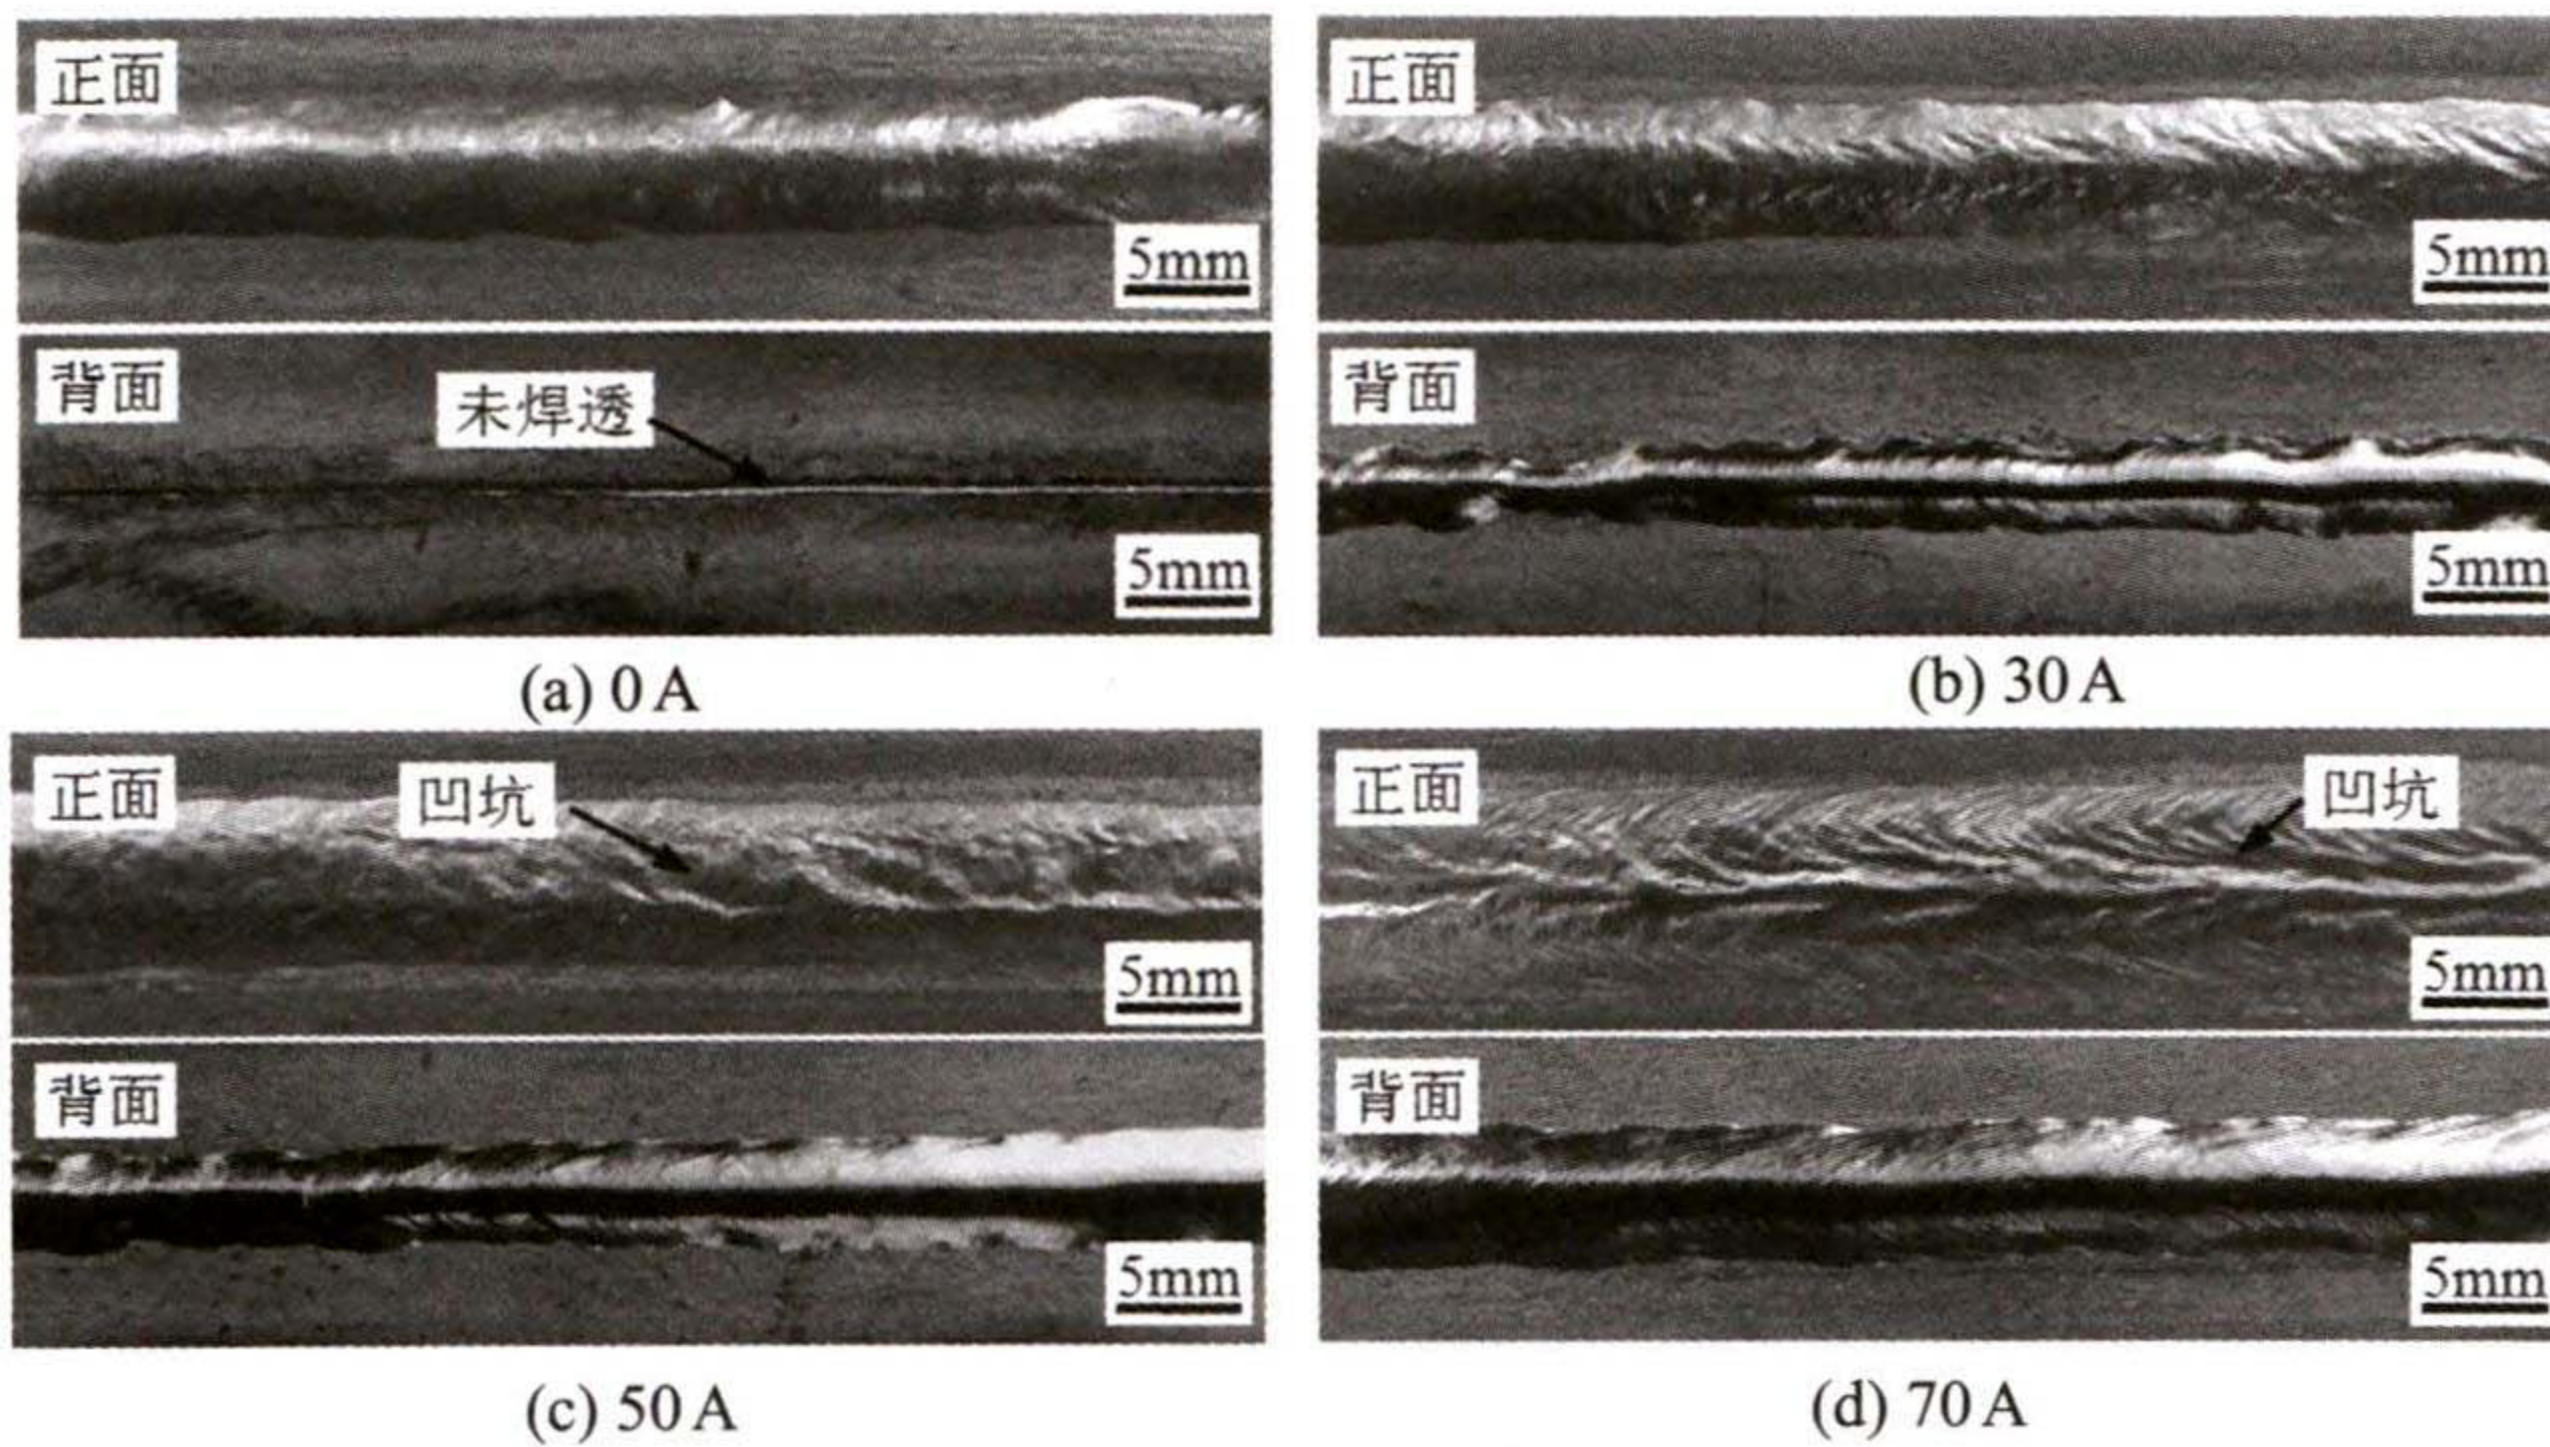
不同电流下激光-TIG复合焊接头的表面形貌
